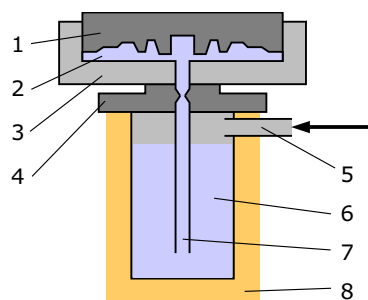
rfZ) 1 Oberform 2 Werkstück 3 Unterform 4 Deckel 5 Druckluft 6 Schmelze 7 Steigrohr 8 Ofen
